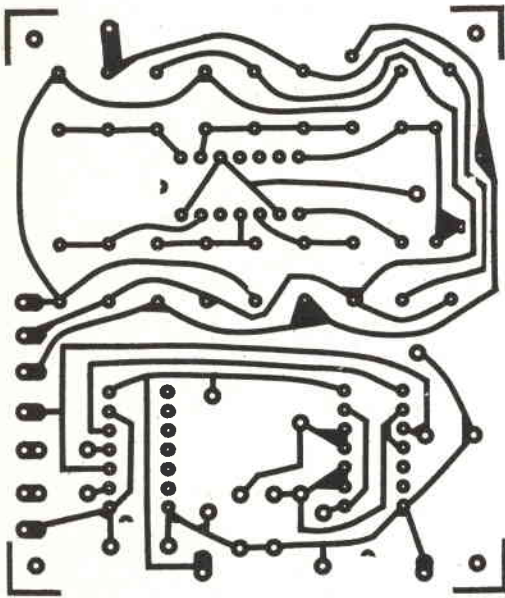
Disposizione dei collegamenti in rame sulla basetta di supporto su cui può essere montato lo strumento di figura 6.
